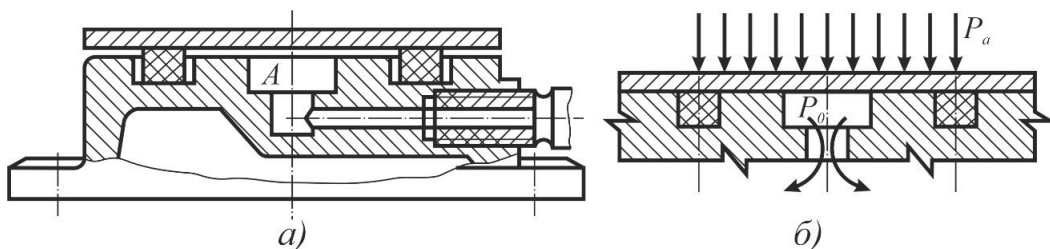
Схема вакуумного привода: а – конструктивное исполнение; б – схема действия усилий зажима
